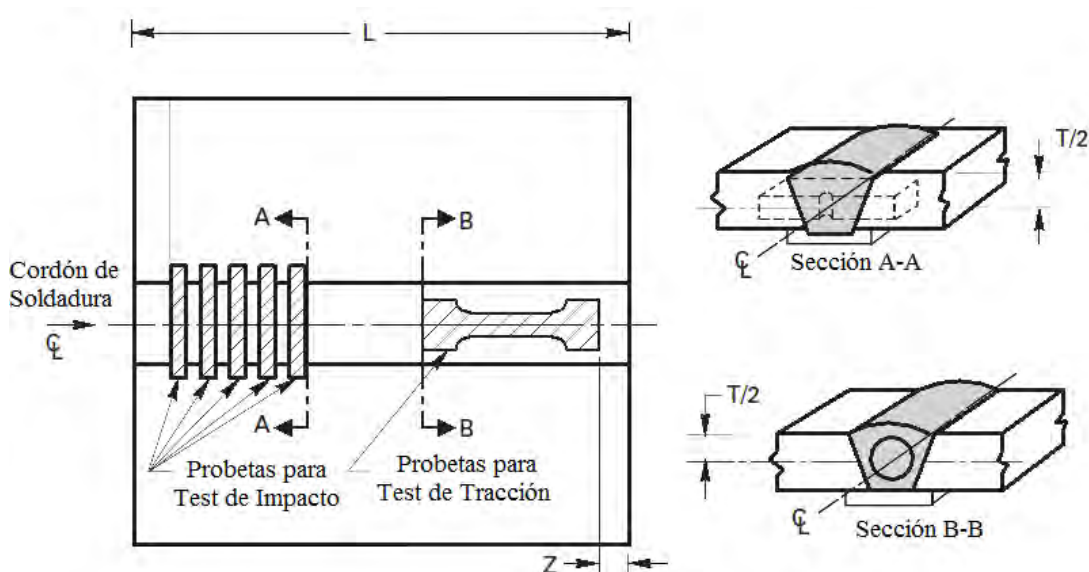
Principales ensayos mecánicos para evaluar la soldadura.
